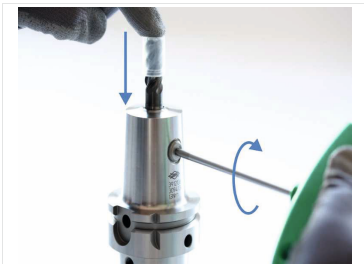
Werkzeug andrücken und Spansschraube anziehen
